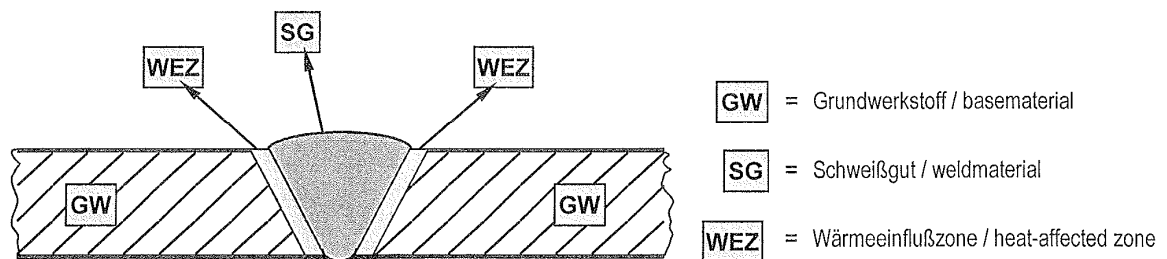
Punkte der durchzuführenden Härtemessung einer Schweißnaht
